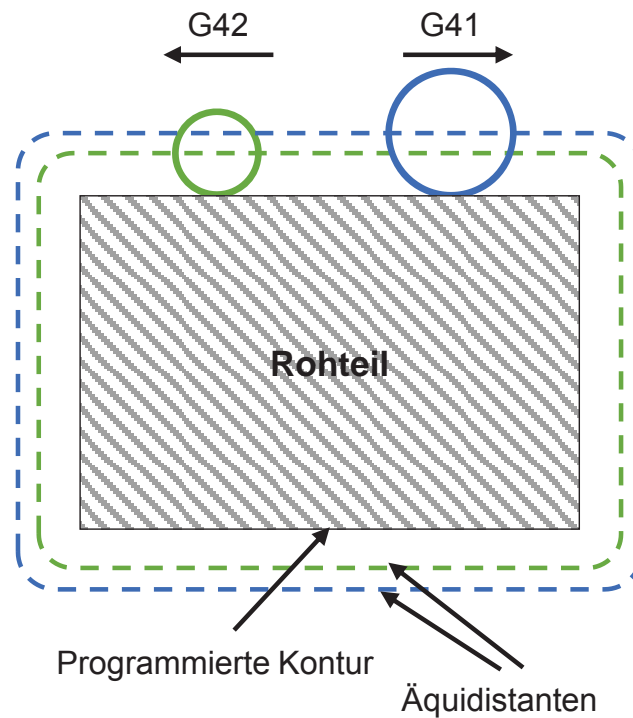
G-Worte der Fräserradiuskompensation
